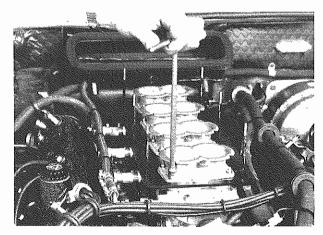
Smontaggio delle prese aria a trombetta Removing air intake manifolds
